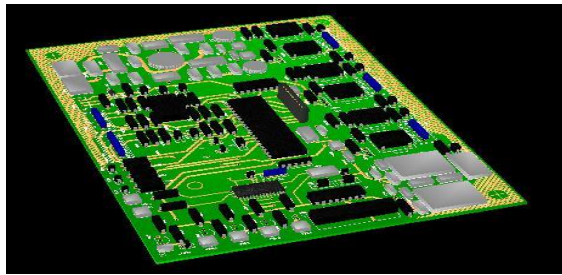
PCB Vista superior 3D, del regulador en Protel. 18X13 cm.
